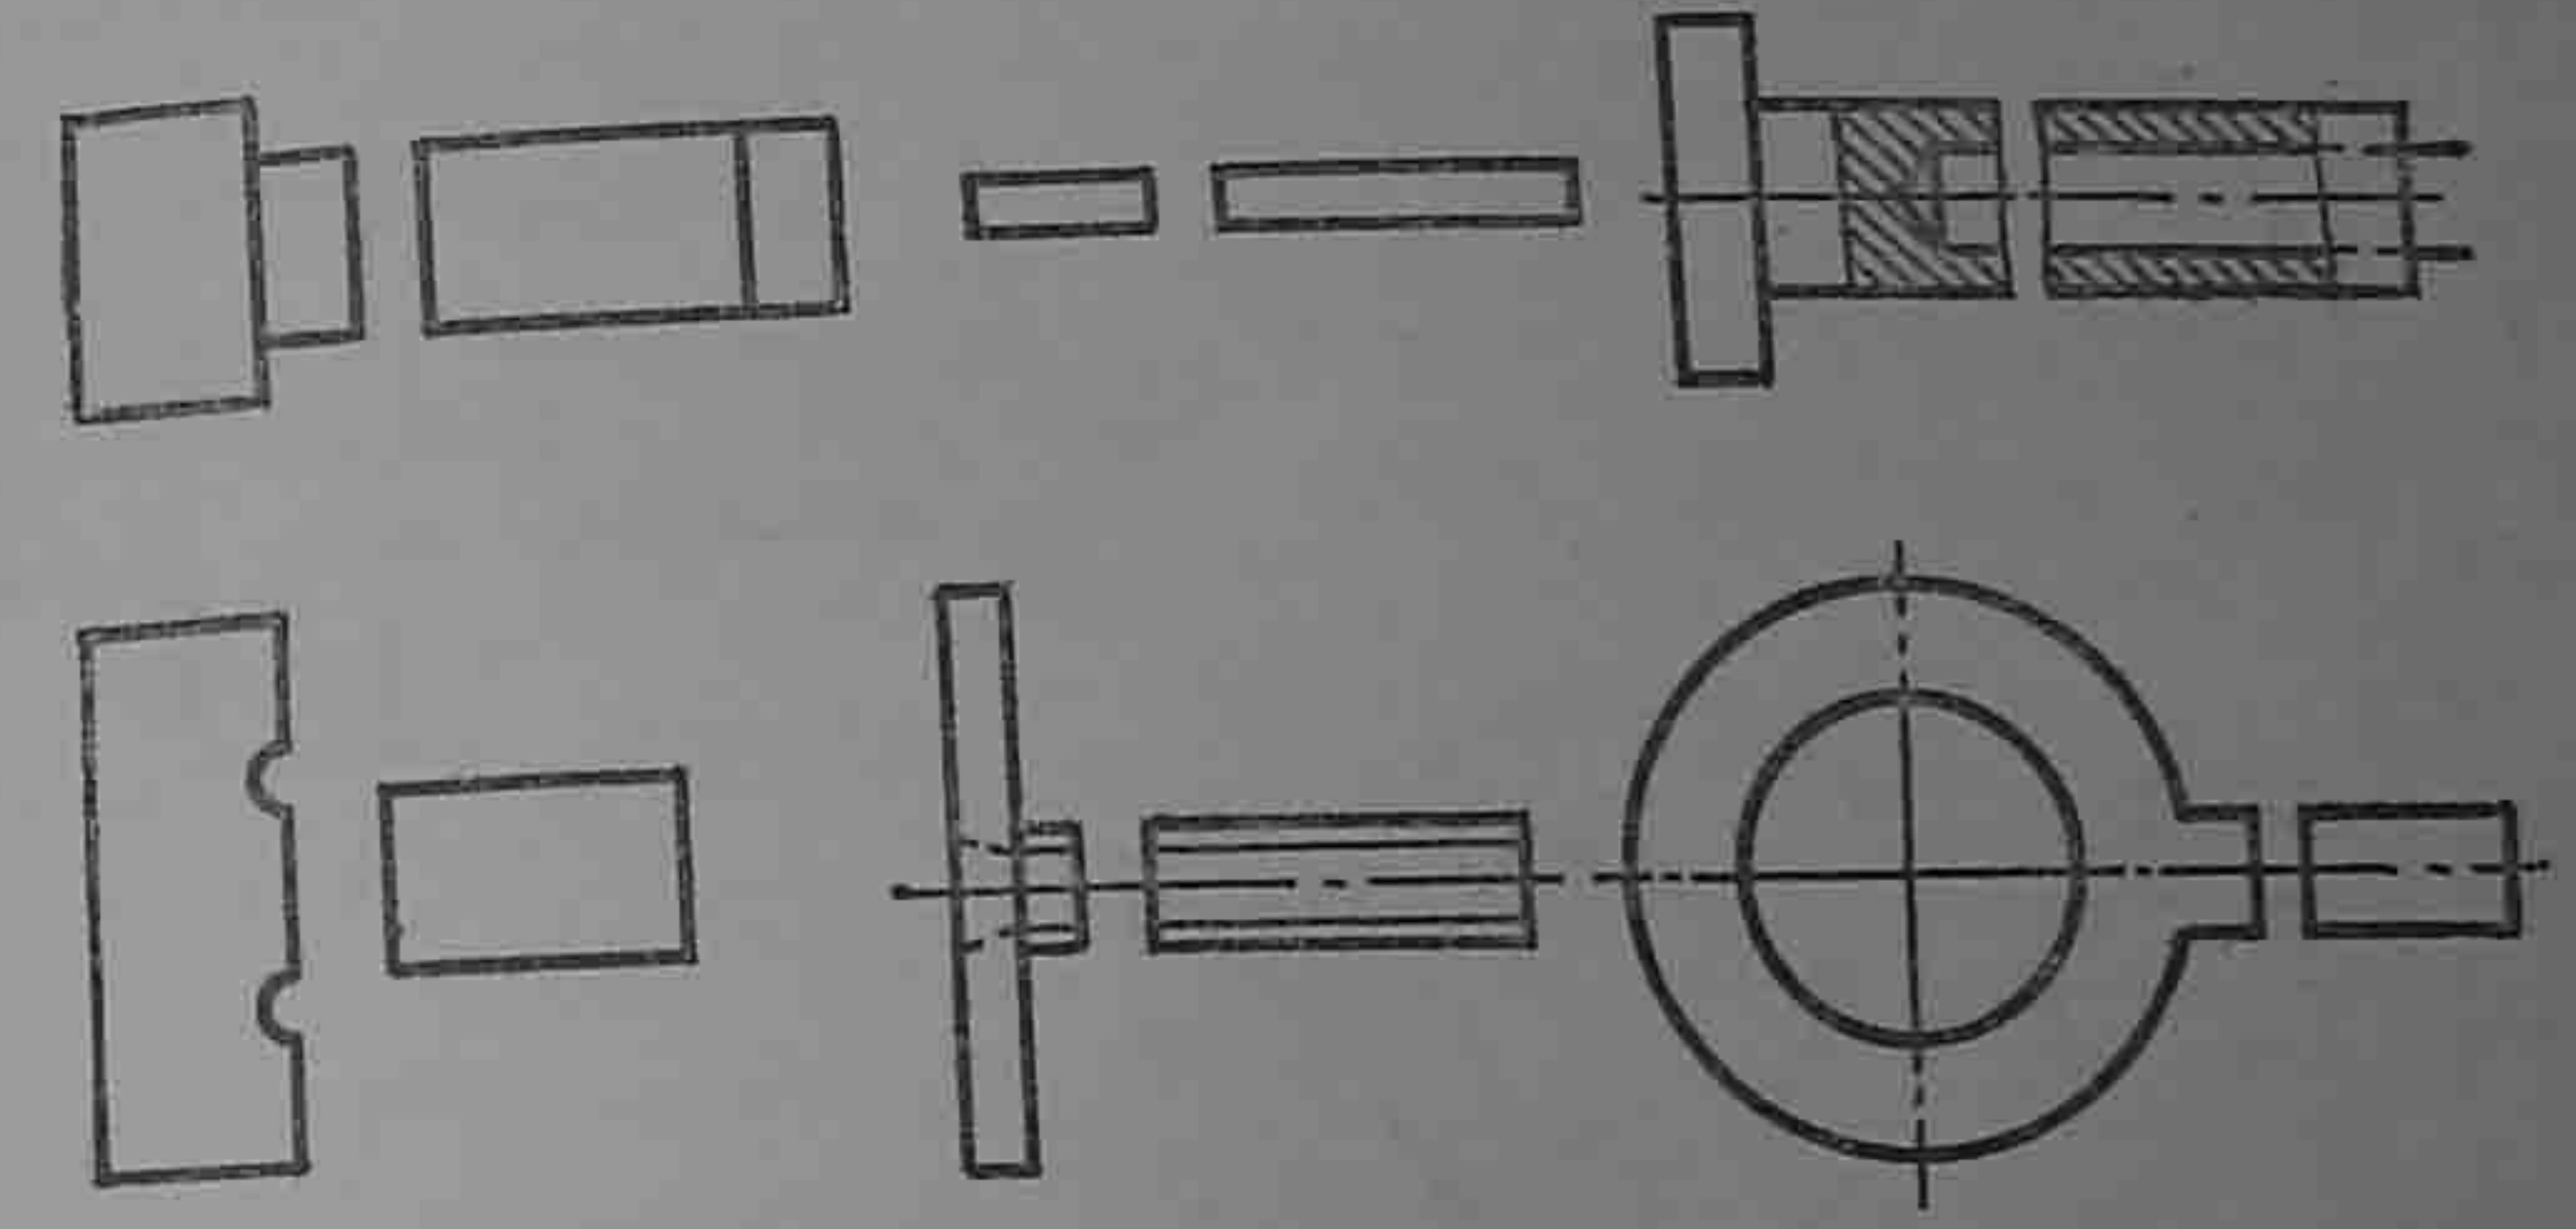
Типы сварных соединений стыковой сварки сопротивлением
